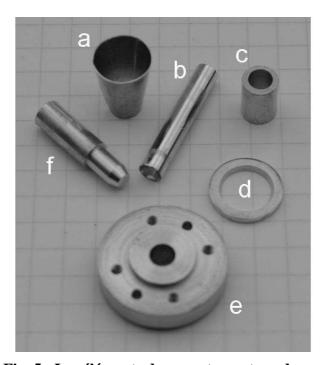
Les éléments du cornet avant soudure.
